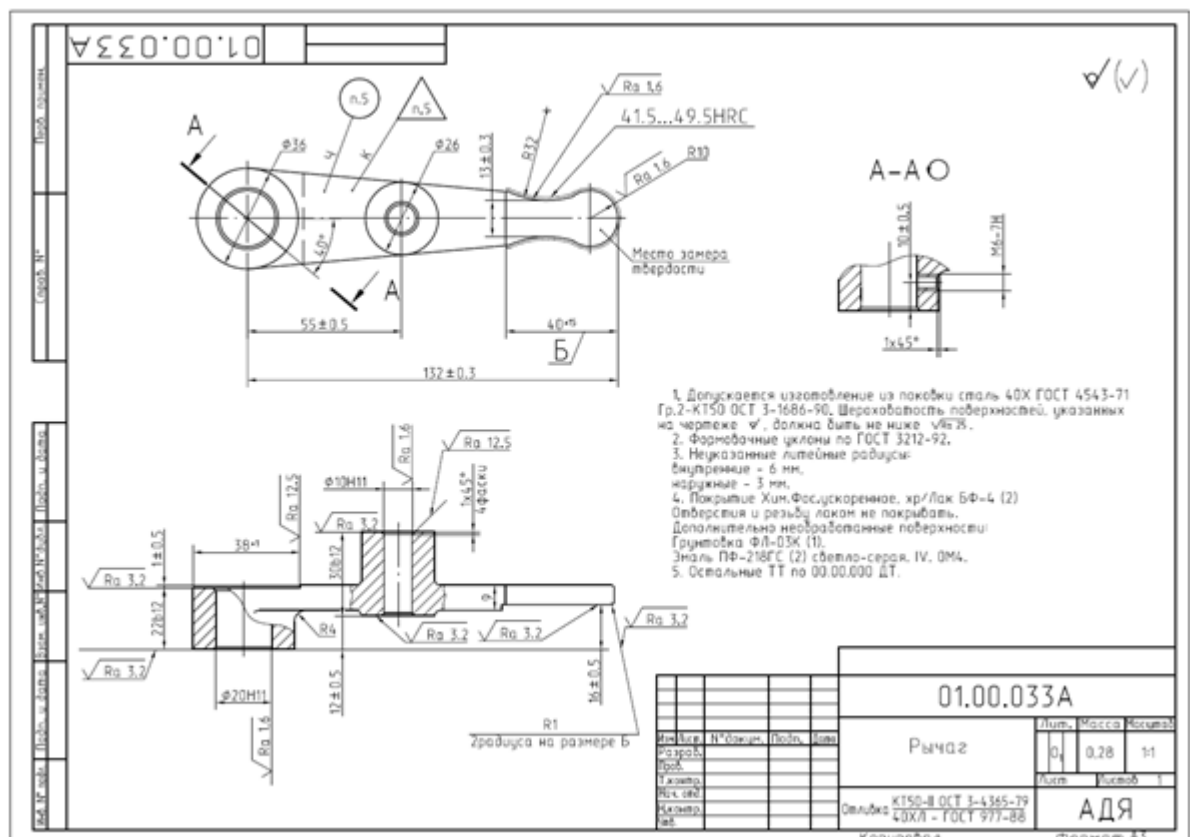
Технический многовидовый чертеж детали 5 «Рычаг»
